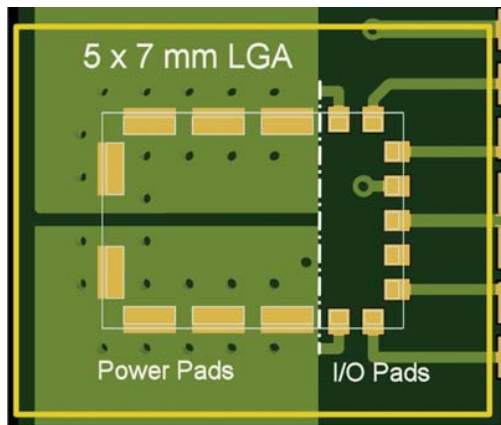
典型的 5 x 7mm LGA 受体 PCB 布局. 预留重焊时的清空边界。
